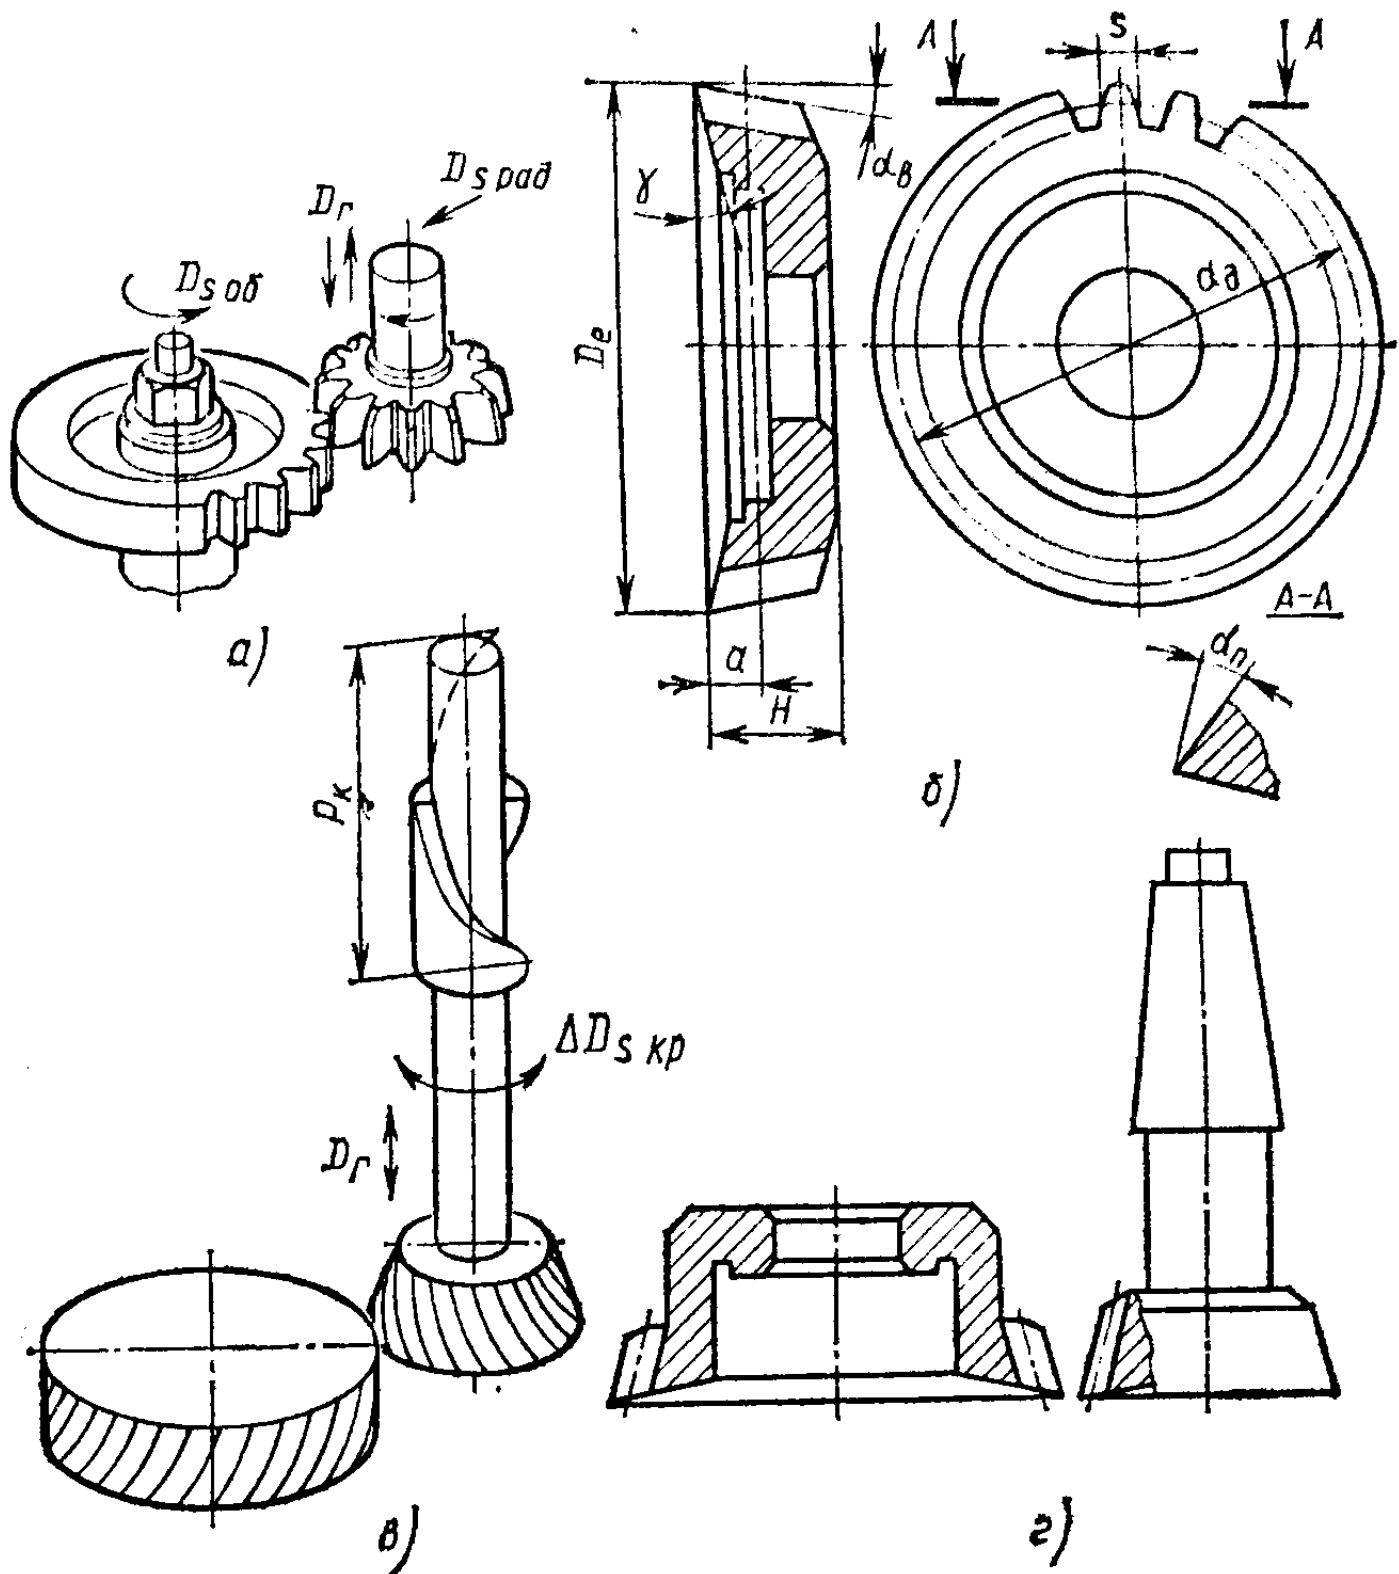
Схемы работы и конструкции зуборезных долбяков
